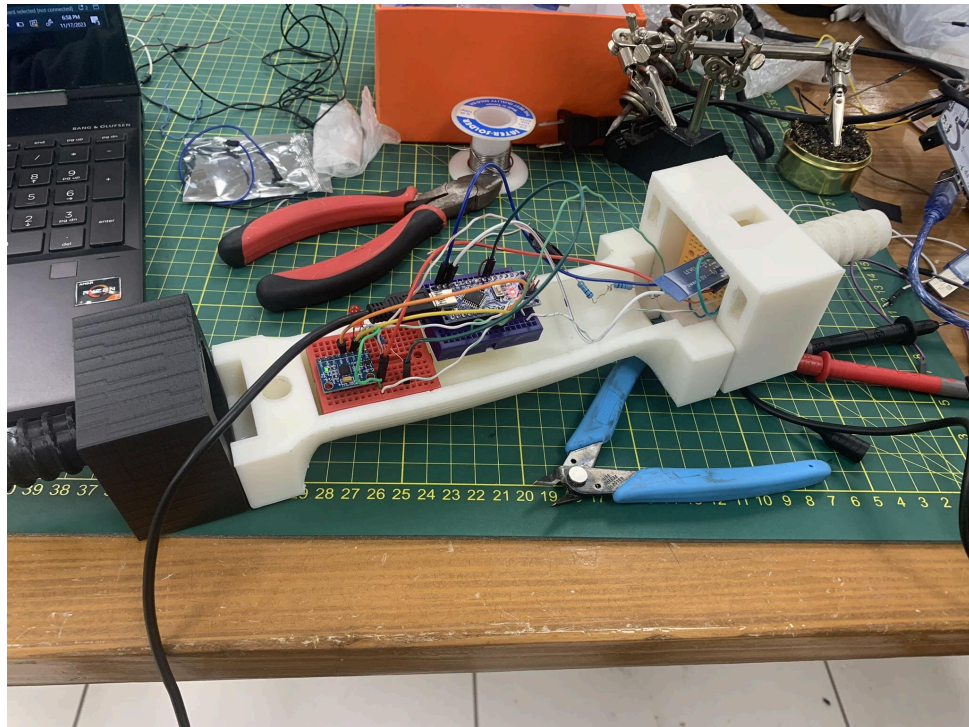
Ensamblaje de piezas impresas en 3D con la circuitería
